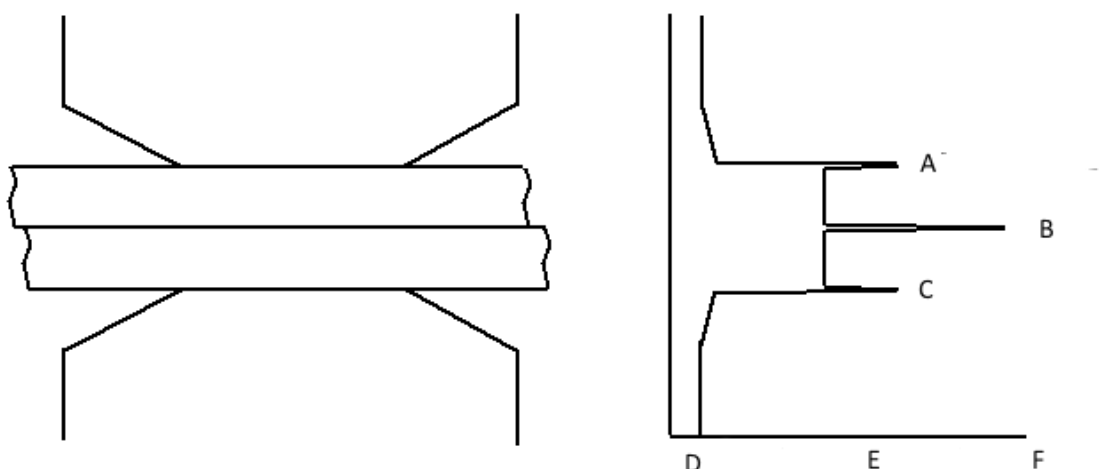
Resistencias del material y de la interfase antes de la soldadura. Contacto de electrodo, B. Interfaz de hoja, C. Contacto de electrodo, D. Bajo, E. Resistencia, F. Alto. Fuente: TWI
